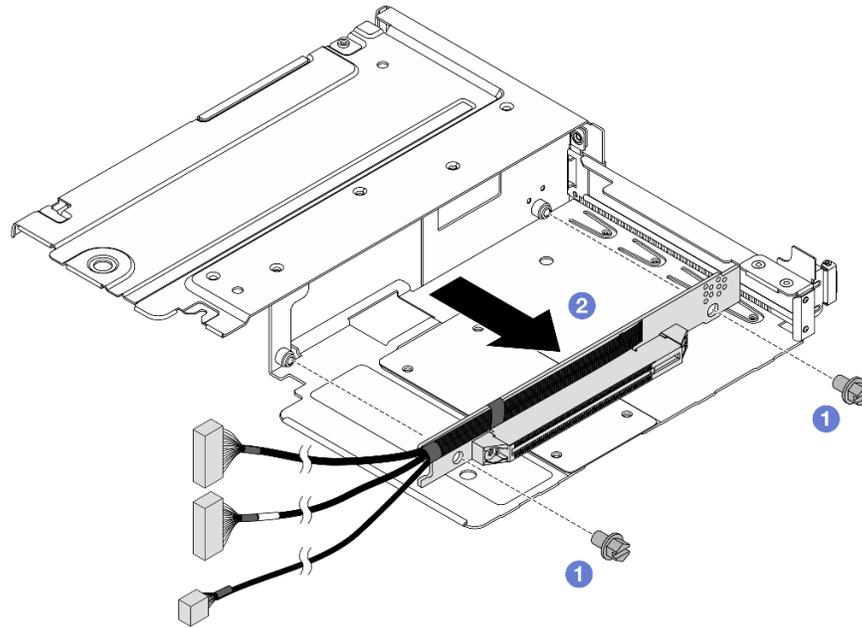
Retrait de la carte mezzanine du boîtier pleine hauteur
